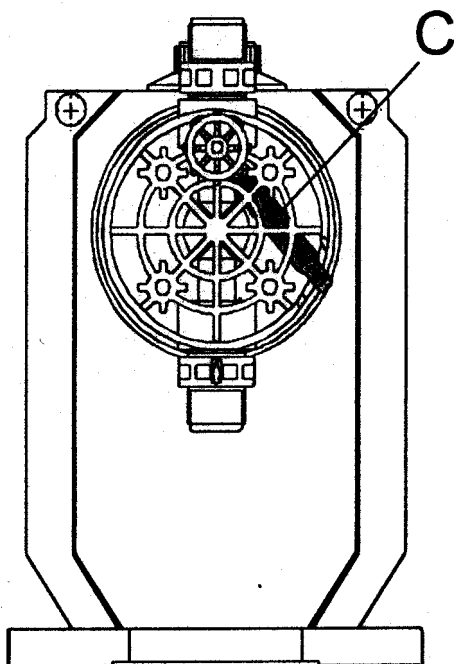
Подсоединение всасывающего, напорного и вентиляционного трубопроводов
